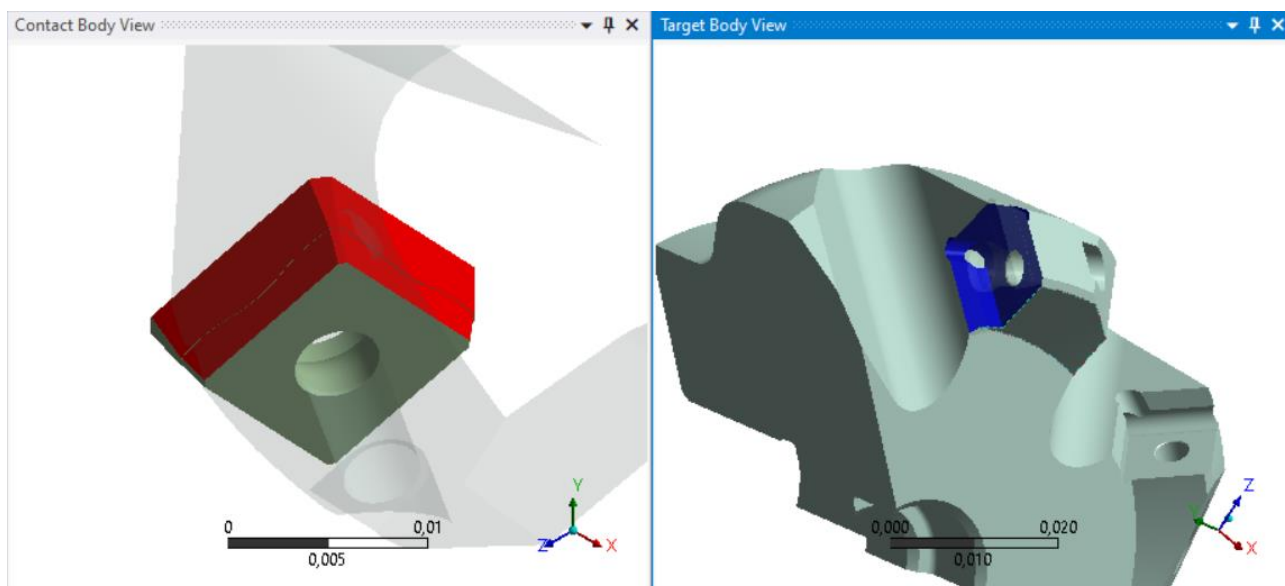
Контакт поверхности пластины и гнезда корпуса
